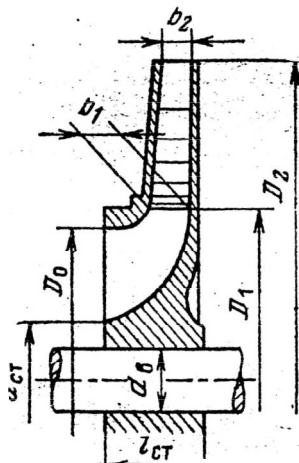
Розрахункова конструктивна схема перерізу робочого колеса
